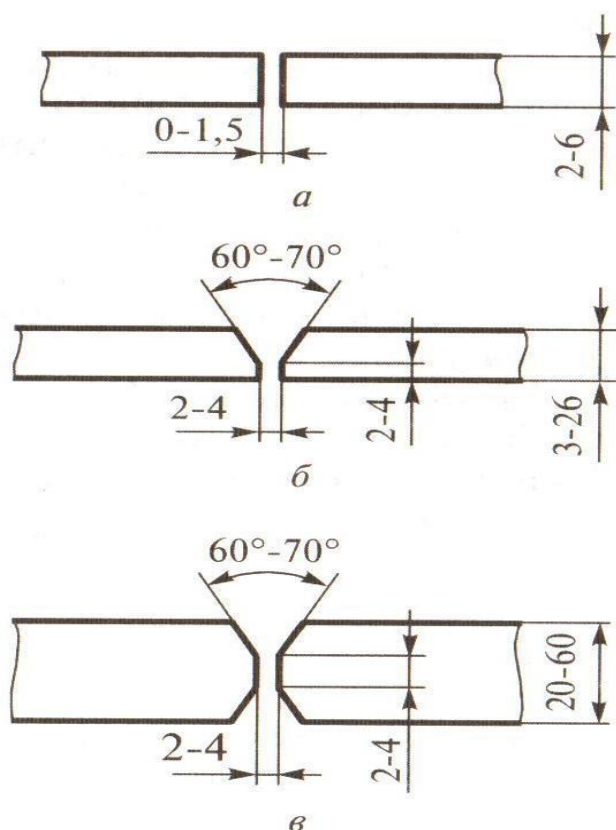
Способи підготовки кромки для стикових з'єднань під час дугового електрозварювання:
